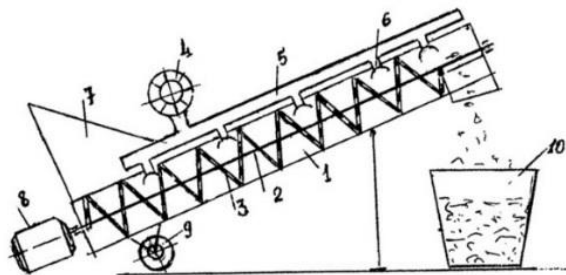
Сушилка для заготавливаемых сине-зеленых водорослей[10]: 1-цилиндрическая полость элеватора; 2-шнек со спиральными лентами -3; 4-нагреватель воздуха; 5-распределитель теплого воздуха; 6-воздушные каналы; 7-загрузочный бункер; 8-электродвигатель привода шнека; 9-колеса для передвижения; 10-контейнер.
